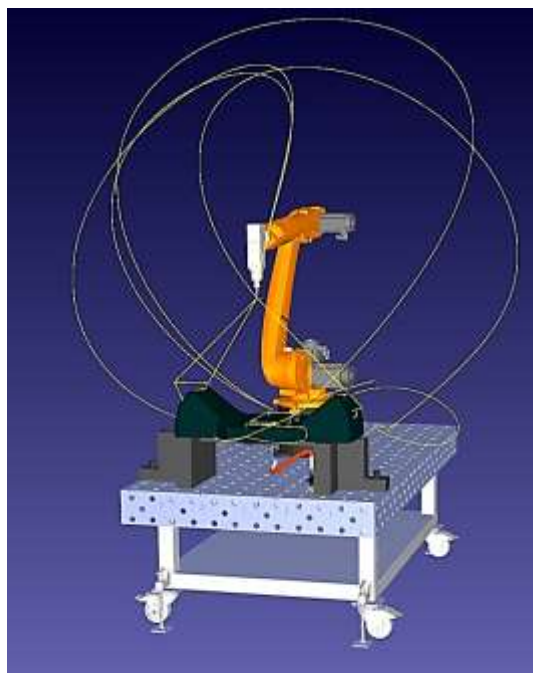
Траектория перемещения инструмента промышленным роботом для фрезерной обработки детали «кожух» (общий вид)
